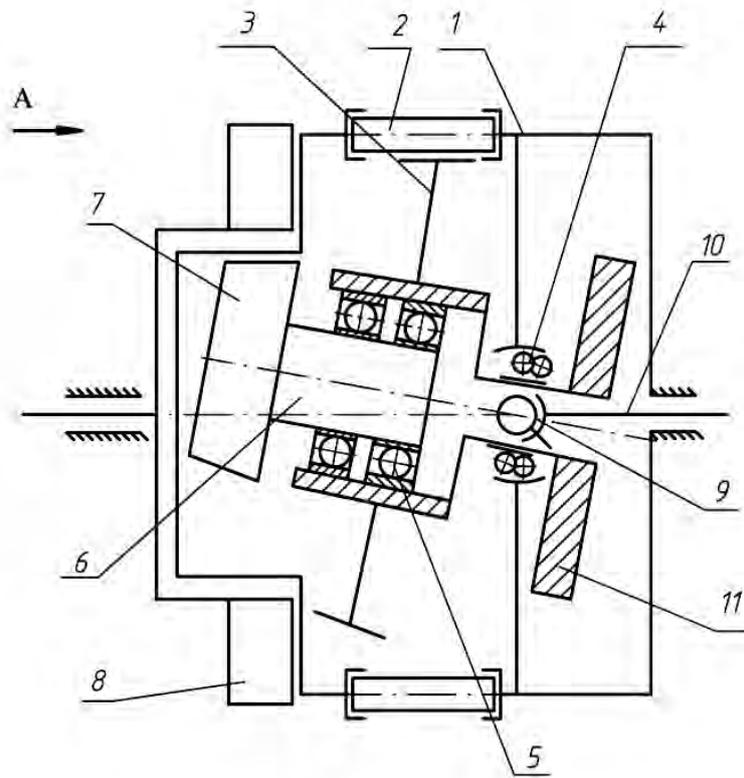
Схема планетарного магнитного привода, разработанная на базе передачи К-Н-V
